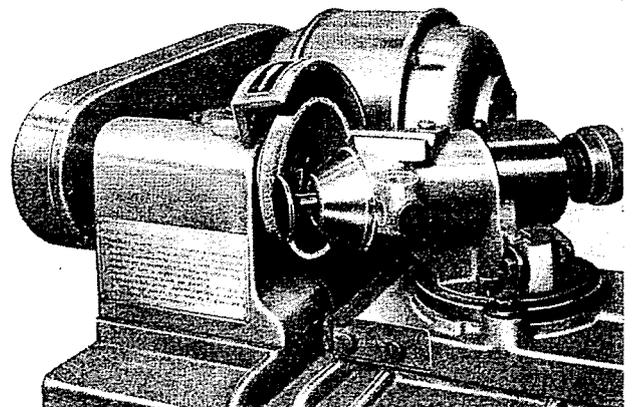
Ventiltellerkegel auf der Universal-Schleifmaschine A. 11401 nachschleifen.
